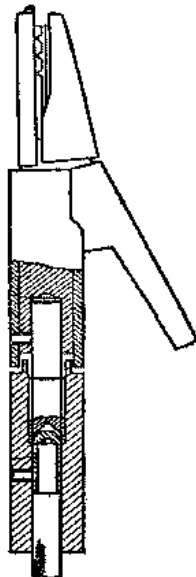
Электродержатель, оборудованный системой ручного отключения тока
